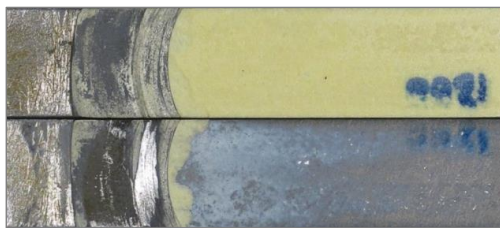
Bruchflächen eines gebrochenen TDCB-Probekörpers mit eingeklebter APS WDS. Durch Rissablenkung in den mit Kleber infiltrierte Grenzbereich kam es zur Rissarretierung sowie - infolge der Überlastung der Kleberschicht - zur Mikrorissbildung (unten).
